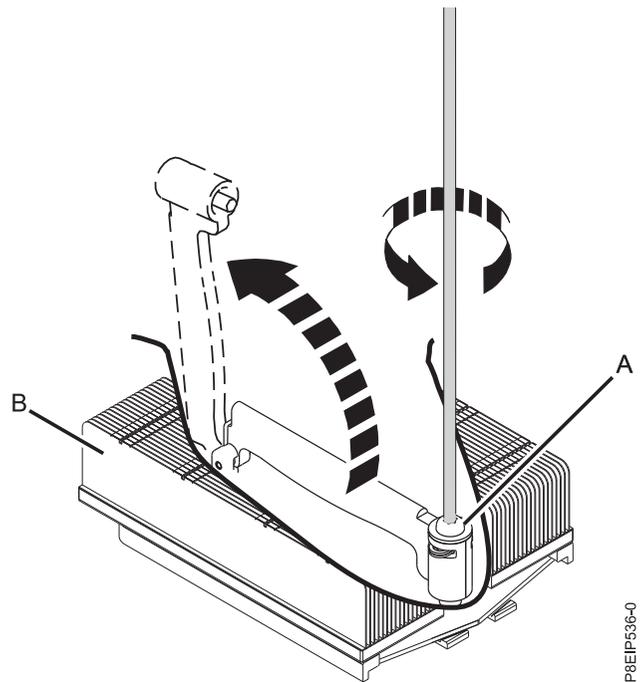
Desserrage de la vis du bras de chargement du dissipateur thermique
